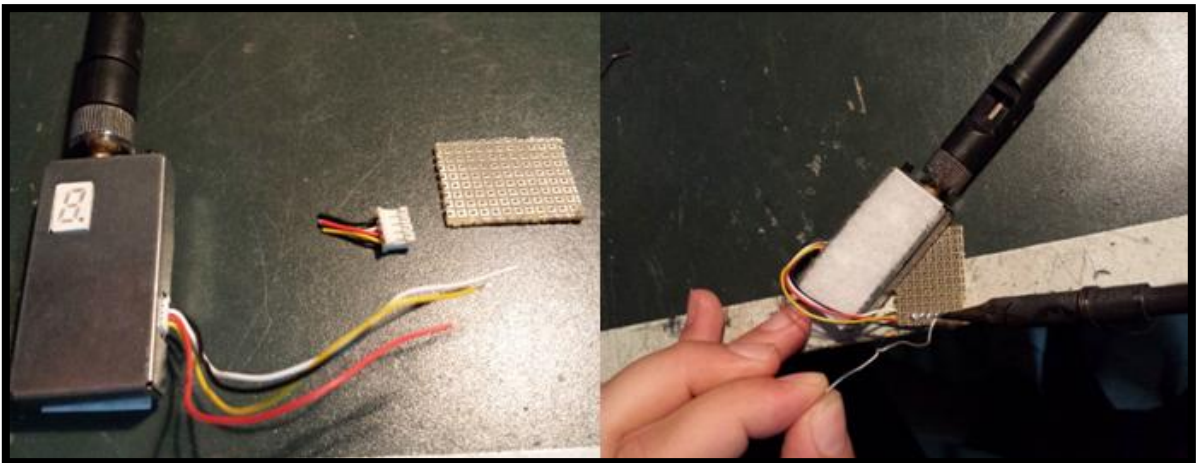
Soldadura de los cables del transmisor de video a la baquelita perforada.
